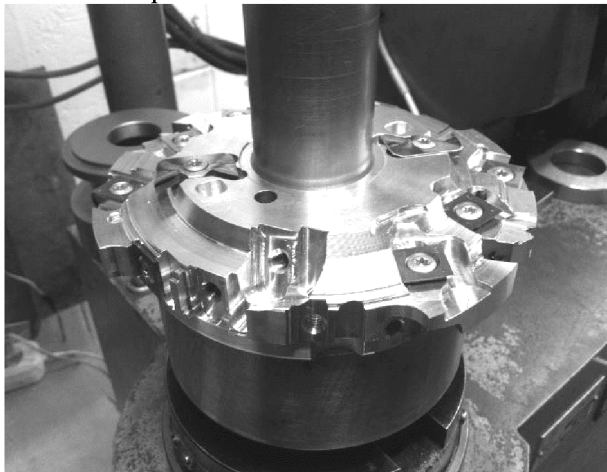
Изготовление корпуса сборной торцевой фрезы для фурнитурного паза с гнездами под СНП (ОАО «ВНИИинструмент»)
